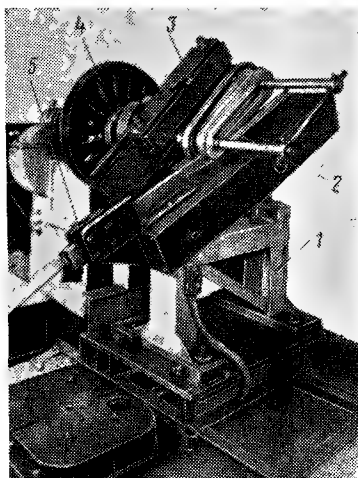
Приспособление для намотки на ребро катушек дополнительных полюсов:
